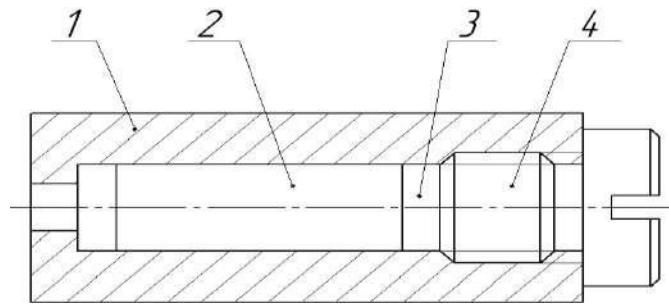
Пристрій для термообробки заготовок ПКМ за умов всебічного стискання: 1 – корпус; 2 – зразок; 3 – диск регулювальний; 4 – кришка
